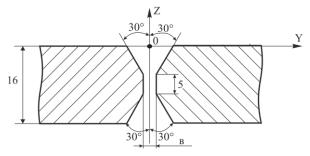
Схема разделки кромок для сварного соединения типа С25.
